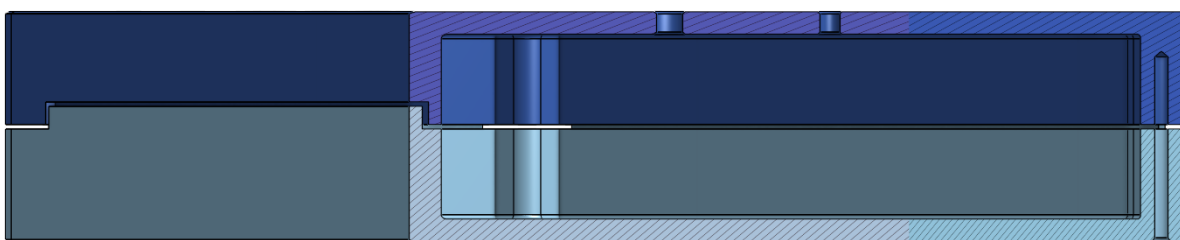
Pohled – půdorys s navigačním plánkem, z Onshape. Foto autor
